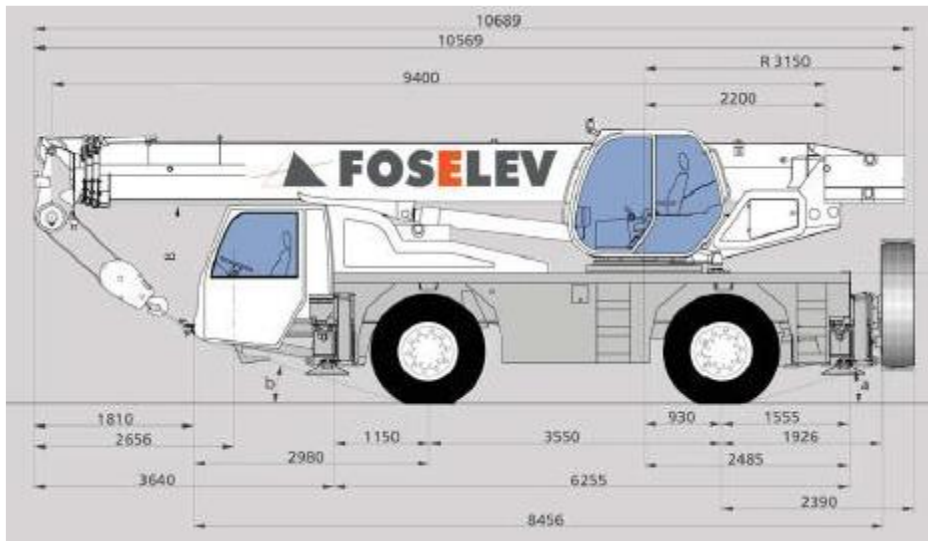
Mobile Crane - Abaque grue 35 Tonnes
